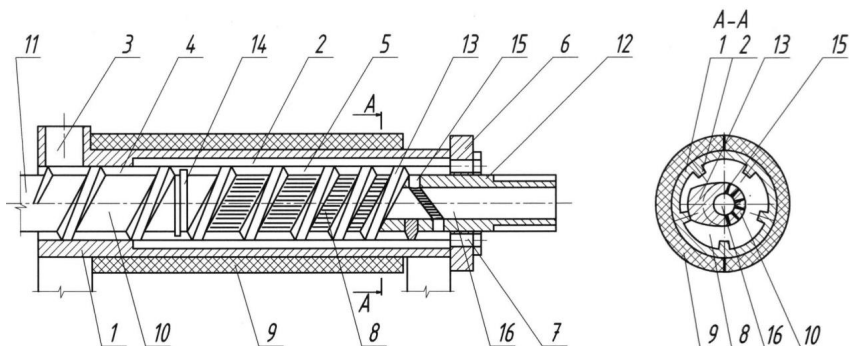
Разрез рабочей камеры установки: 1 рабочая камера; 2-продольные ножи; 3- канал подачи семян; 4 транспортно-размолочная зона; 5-отжимная зона; 6-матрица 7-отверстия для выхода отжимок; 8 полый шнек; 9 нагревательные элементы; 10-вал шнека, 11-приводной конец вала; 12-выходной конец для масла; 13-витки шнека; 14-дробильная насадка; 15-зерновыеотверстия; 16-канал для выхода масла
